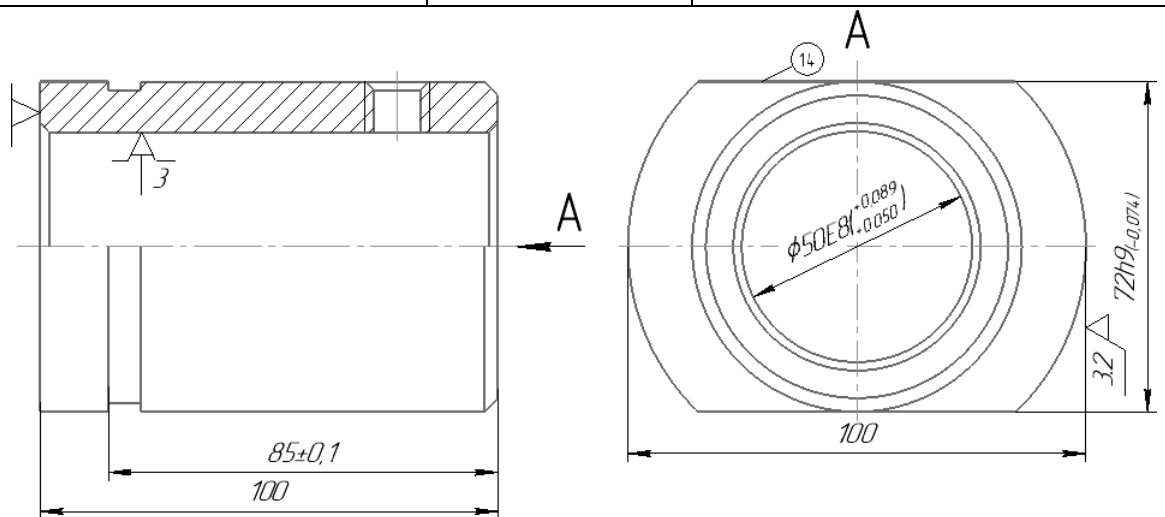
Фрезерування лисок в розмір 72 h9
